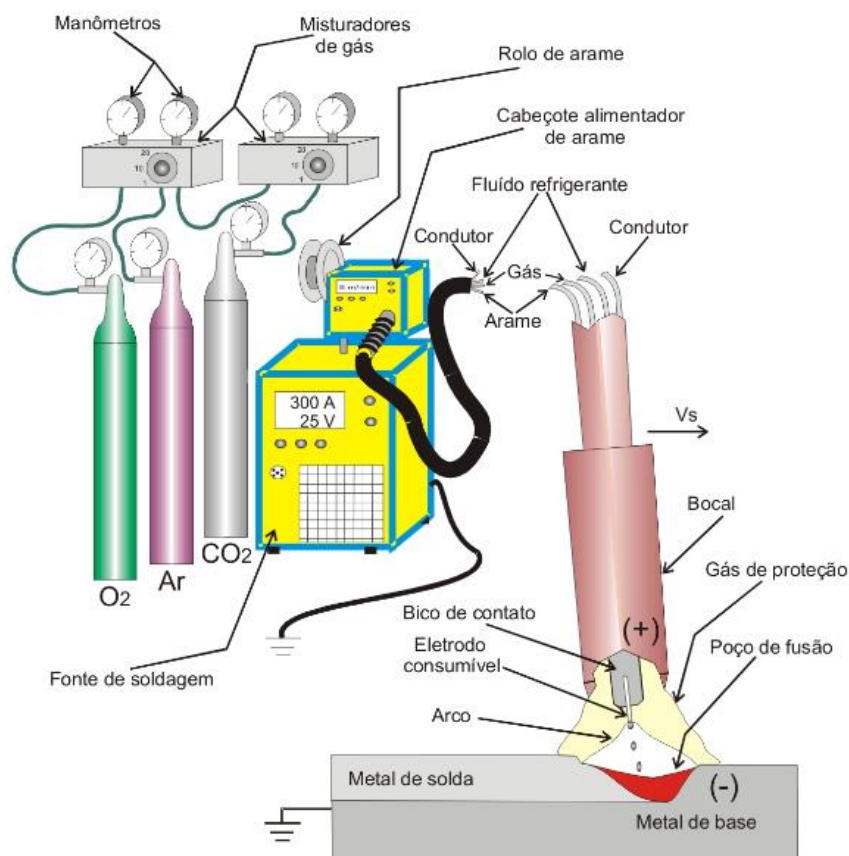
Representação esquemática da soldagem MIG/MAG [9].
